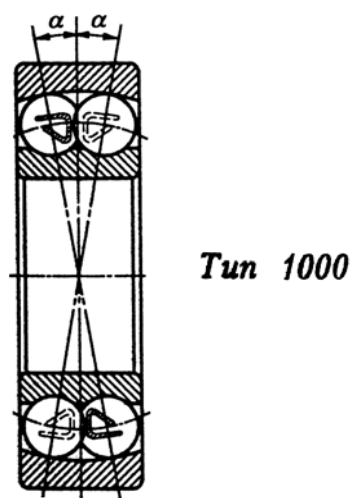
Кульковий підшипник радіальний дворядний сферичний
